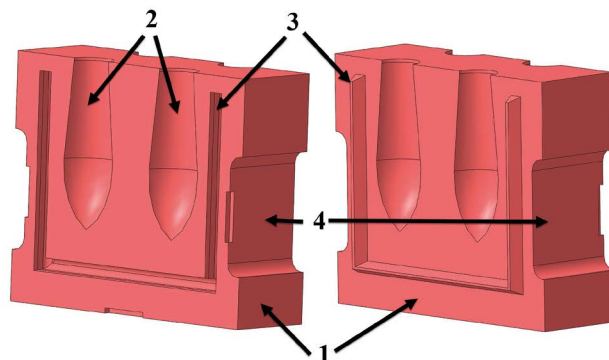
Сегмент формы для отливки суппозитория, вид с двух сторон:
